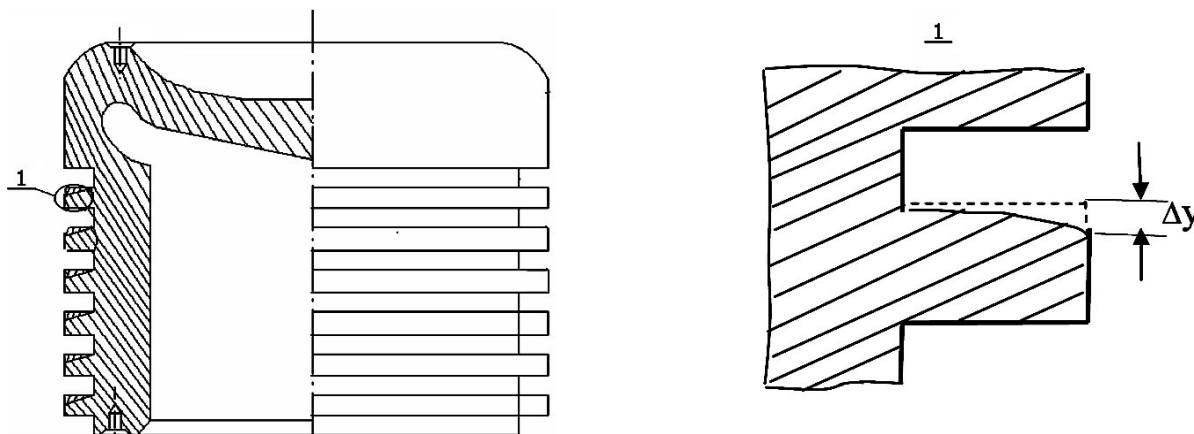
Профиль изношенной опорной торцевой поверхности канавки головки поршня МОД
